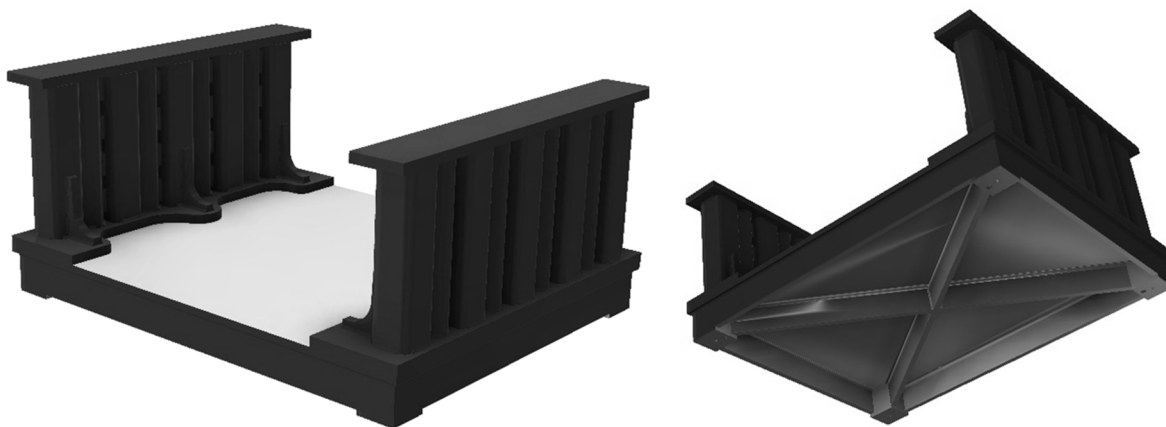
Schematické vyobrazení svařované konstrukce rámu stroje
